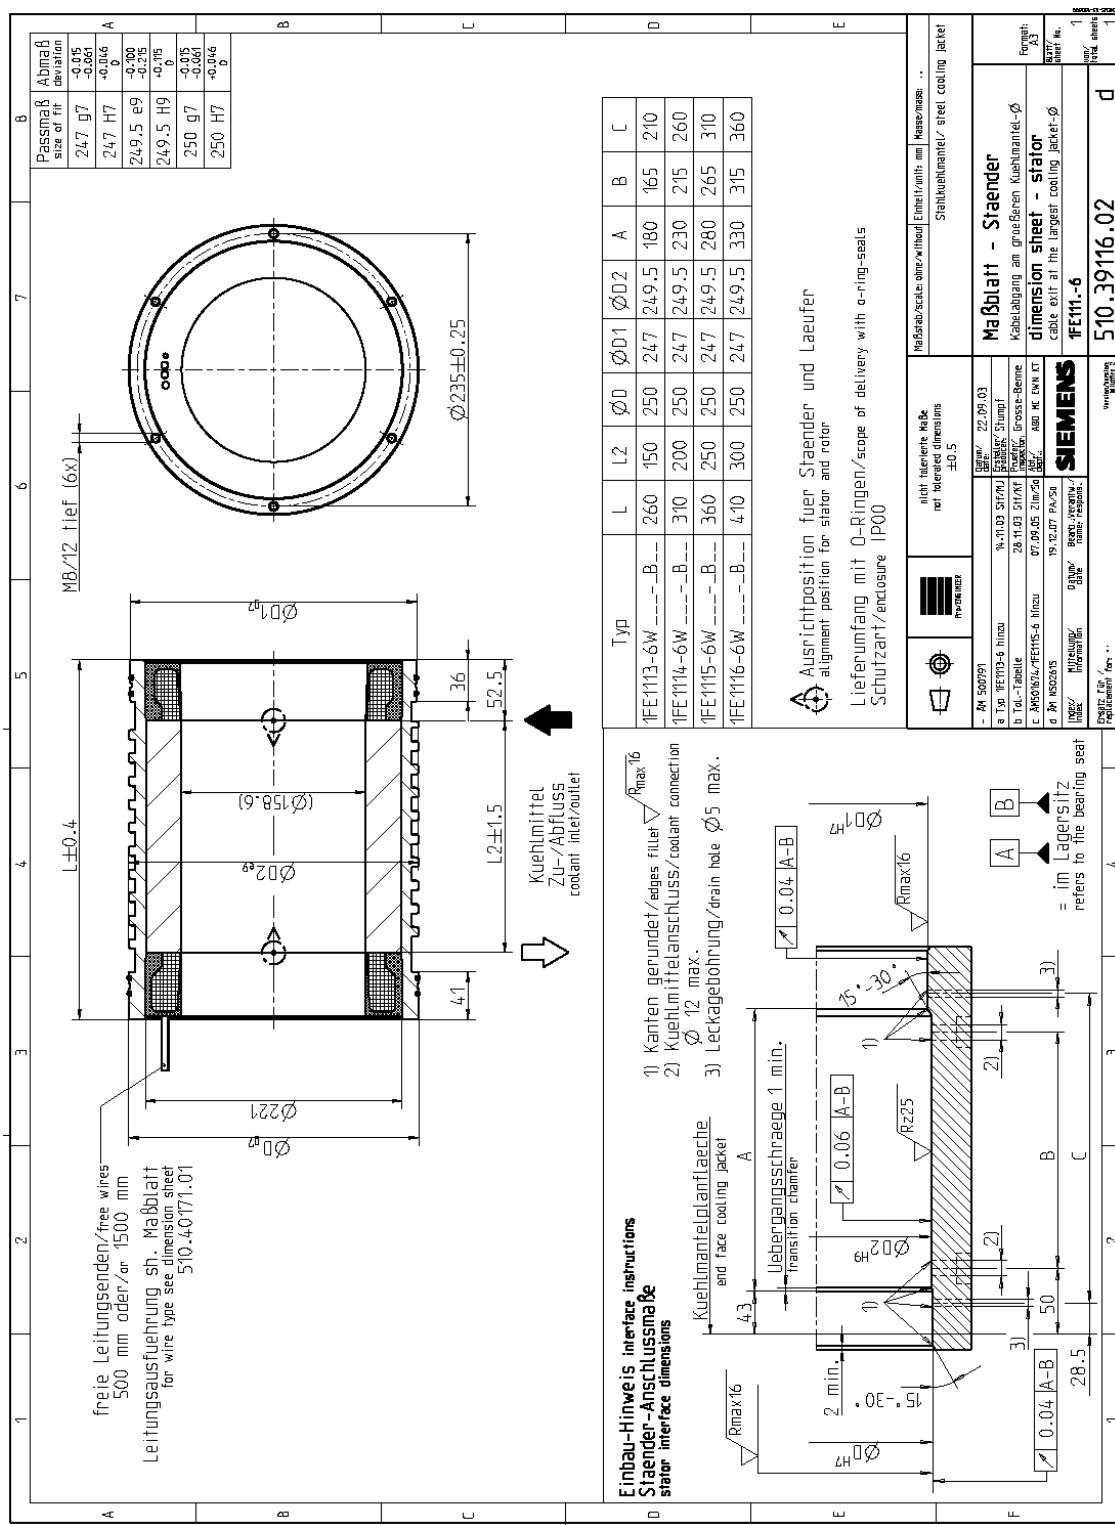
1FE111□-6, Ständer mit Kühlmantel, Kabelabgang am größeren Kühlmanteldurchmesser
